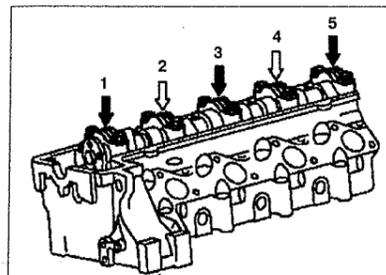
Порядок ослабления и затяжки болтов крепления крышек подшипников распределительного вала.
